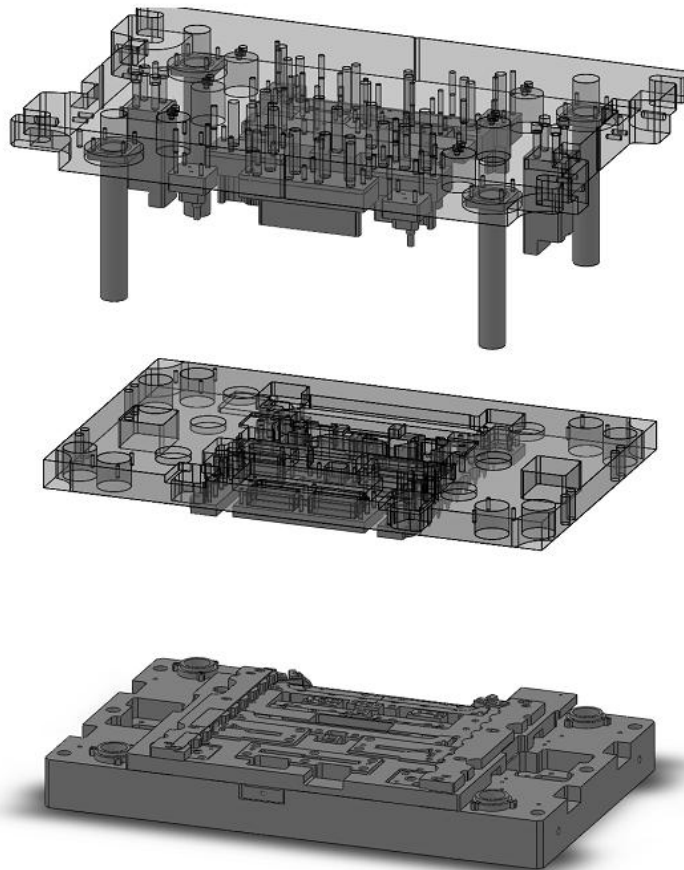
Imagem da ferramenta explodida. Desenhado em Solidworks.
